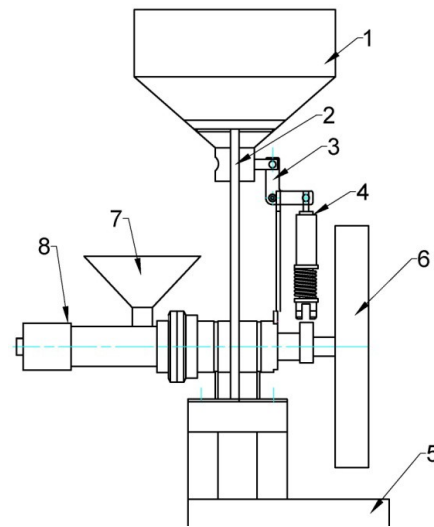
Экструдер ЭК-40: 1 - бункер; 2 - держатель бункера; 3 - механизм подачи смеси; 4 - толкатель; 5 - рама; 6 - ведомое колесо; 7 - приемная воронка; 8 - рабочая часть
